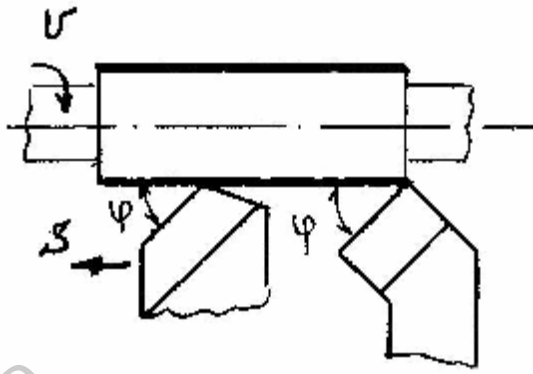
Схема обработки прямыми и отогнутыми проходными резцами
